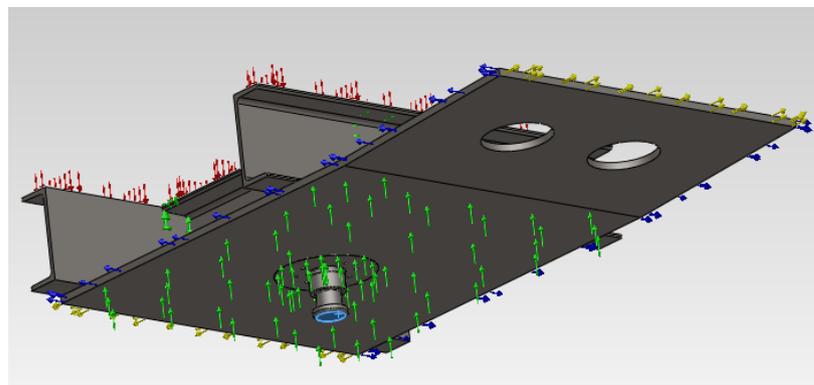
Plancha y refuerzos para King Pin.¹⁰¹
